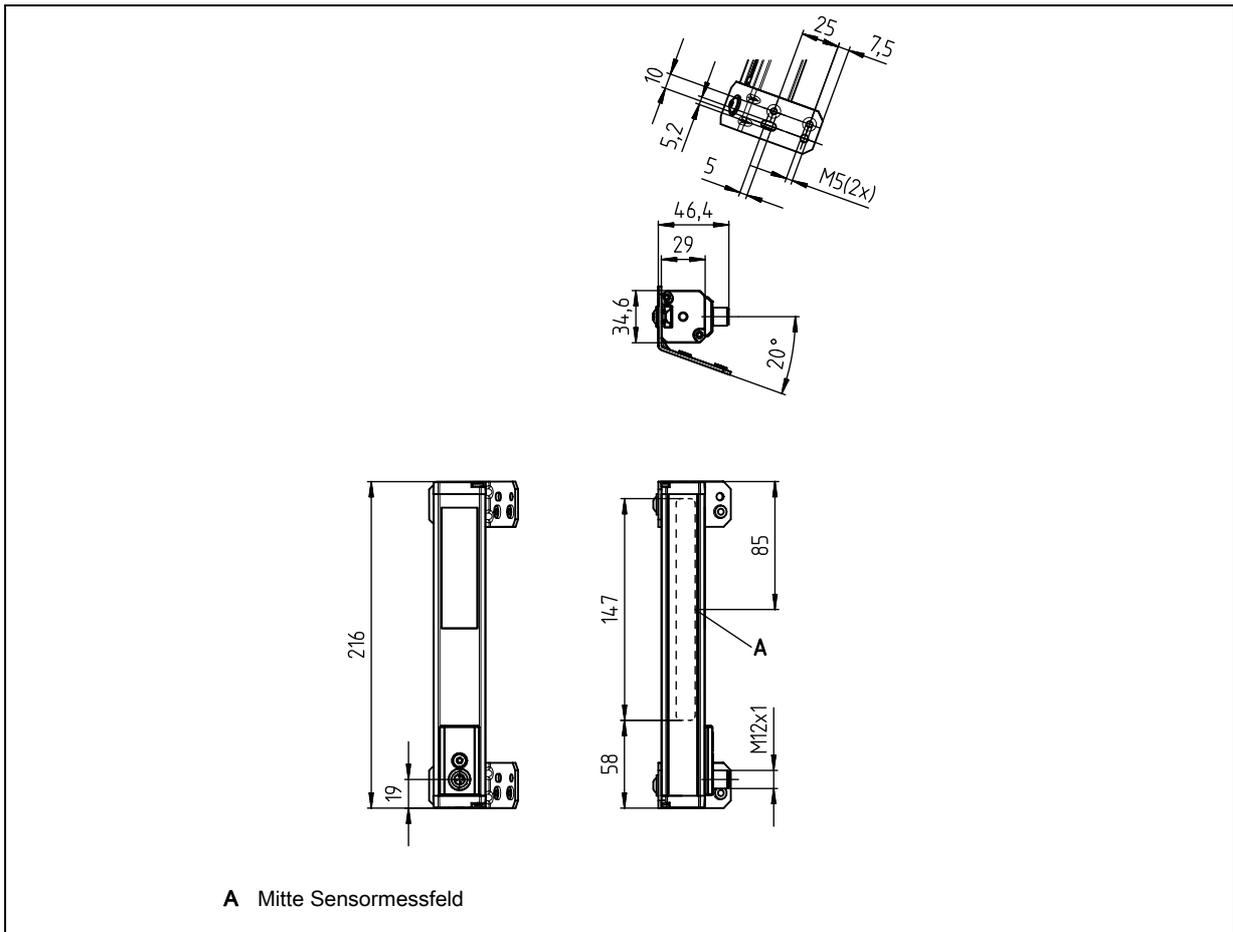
Maßzeichnung OGS 600-140/D...-M12.8 – kurze Ausführung
